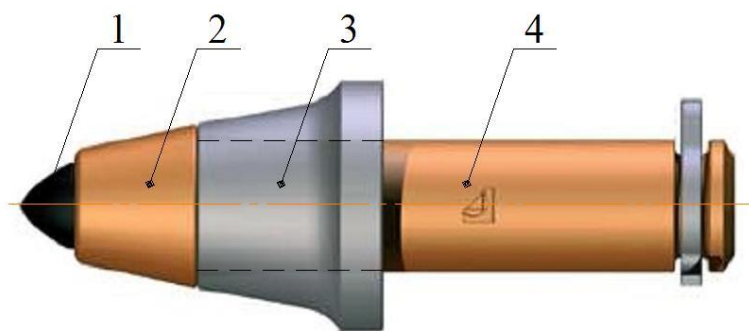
Составной резец РШ С-25-65L72/16SK: 1 – твердосплавная вставка; 2 – головка корпуса; 3 – съемная втулка (опорная зона резца); 4 – хвостовик.
